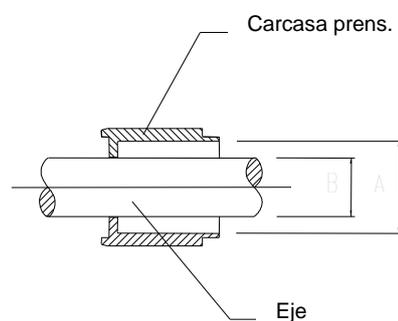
Dimensiones A y B en el eje y la carcasa de la junta del eje.
